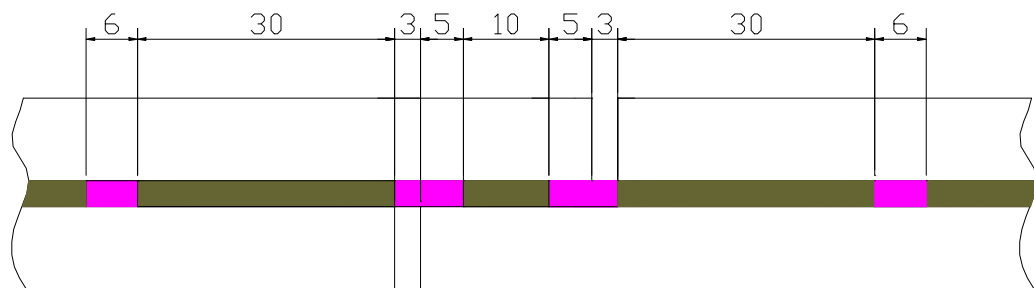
Pormenor da geometria do provete JSS-AE com $L = 10$ mm de sobreposição parcial.
